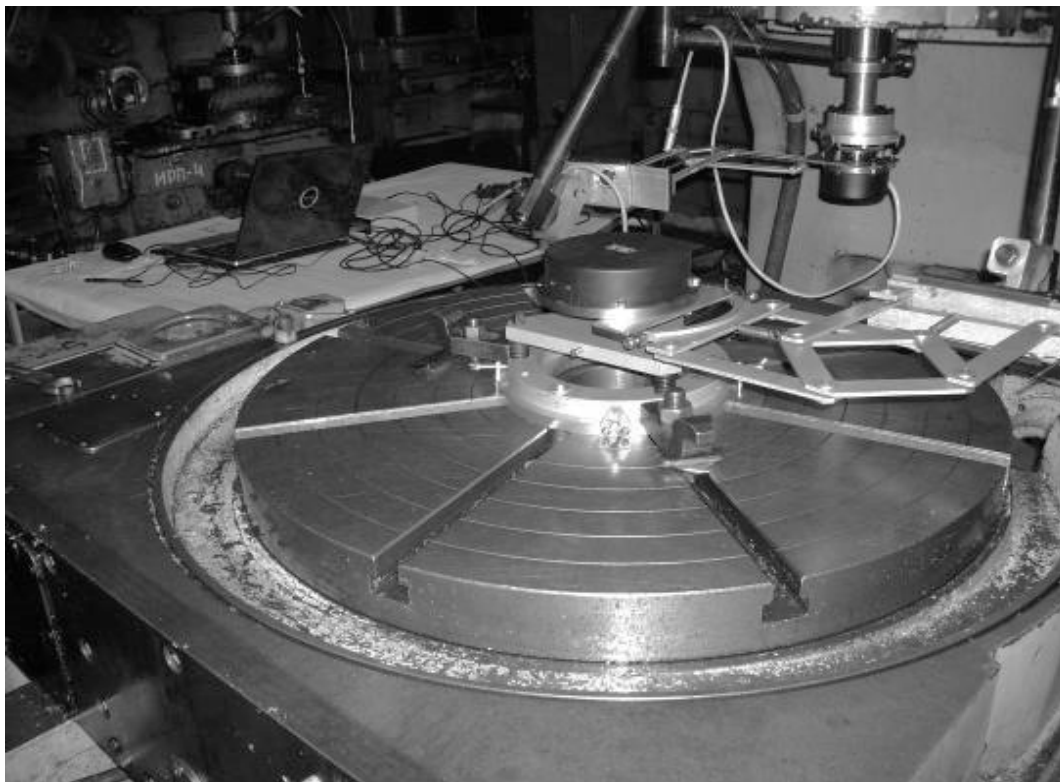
Проверка кинематической точности зубодолбёжного станка мод. 5М150 ПФ
